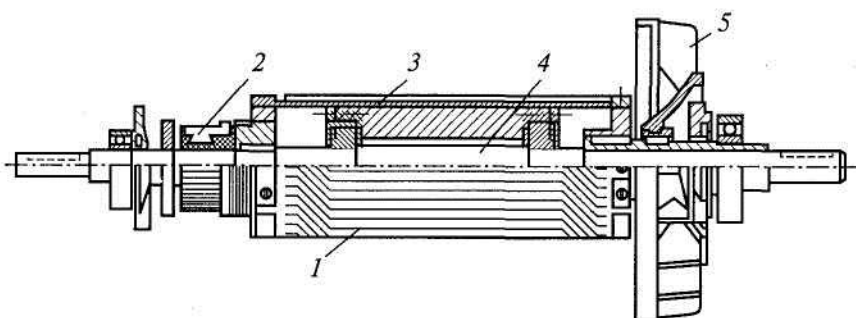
Цилиндрический якорь с печатной обмоткой в сборе:
